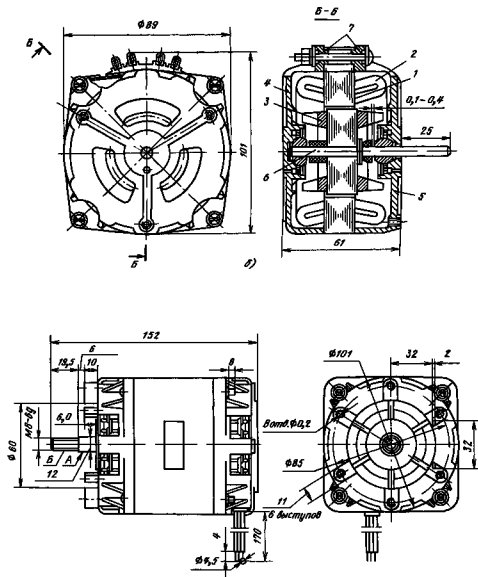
11 Общий вид и габаритные размеры двигателя КД120-4/56РМ6 (форма исполнения 1М3681)
